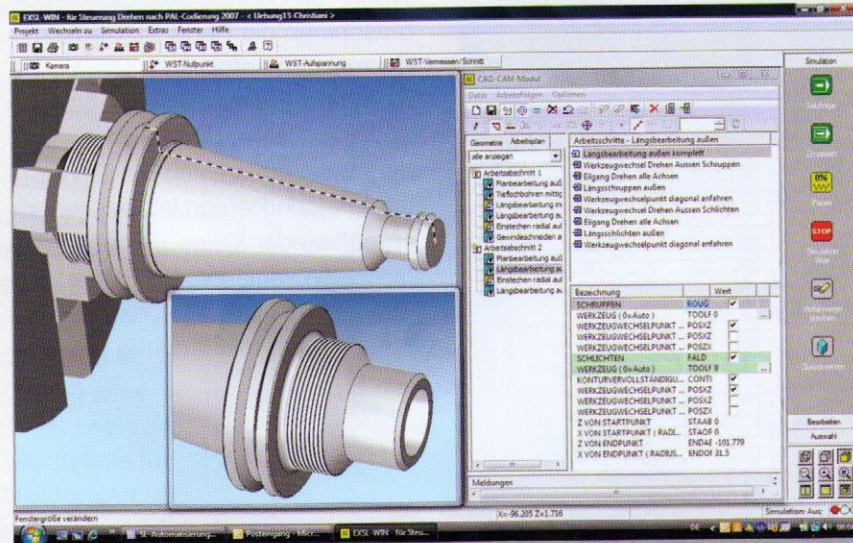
EXSL-CAM / Drehen (Werkbilder: SL-Automatisierungstechnik GmbH, Iserlohn)
